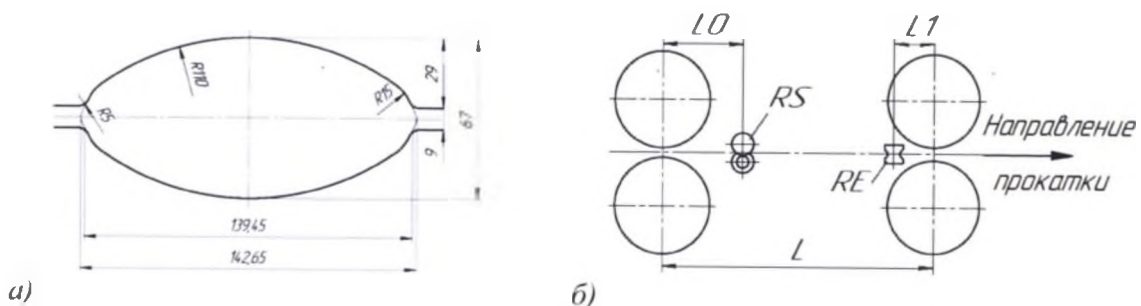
Схема кантовки полосы после клетки №3: а – калибр клетки №3; б – схема установки проводок
